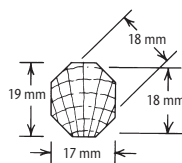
Typisches Sprossenende nach dem Trocknen. Bearbeiten Sie das zu große Maß auf 18 mm.
